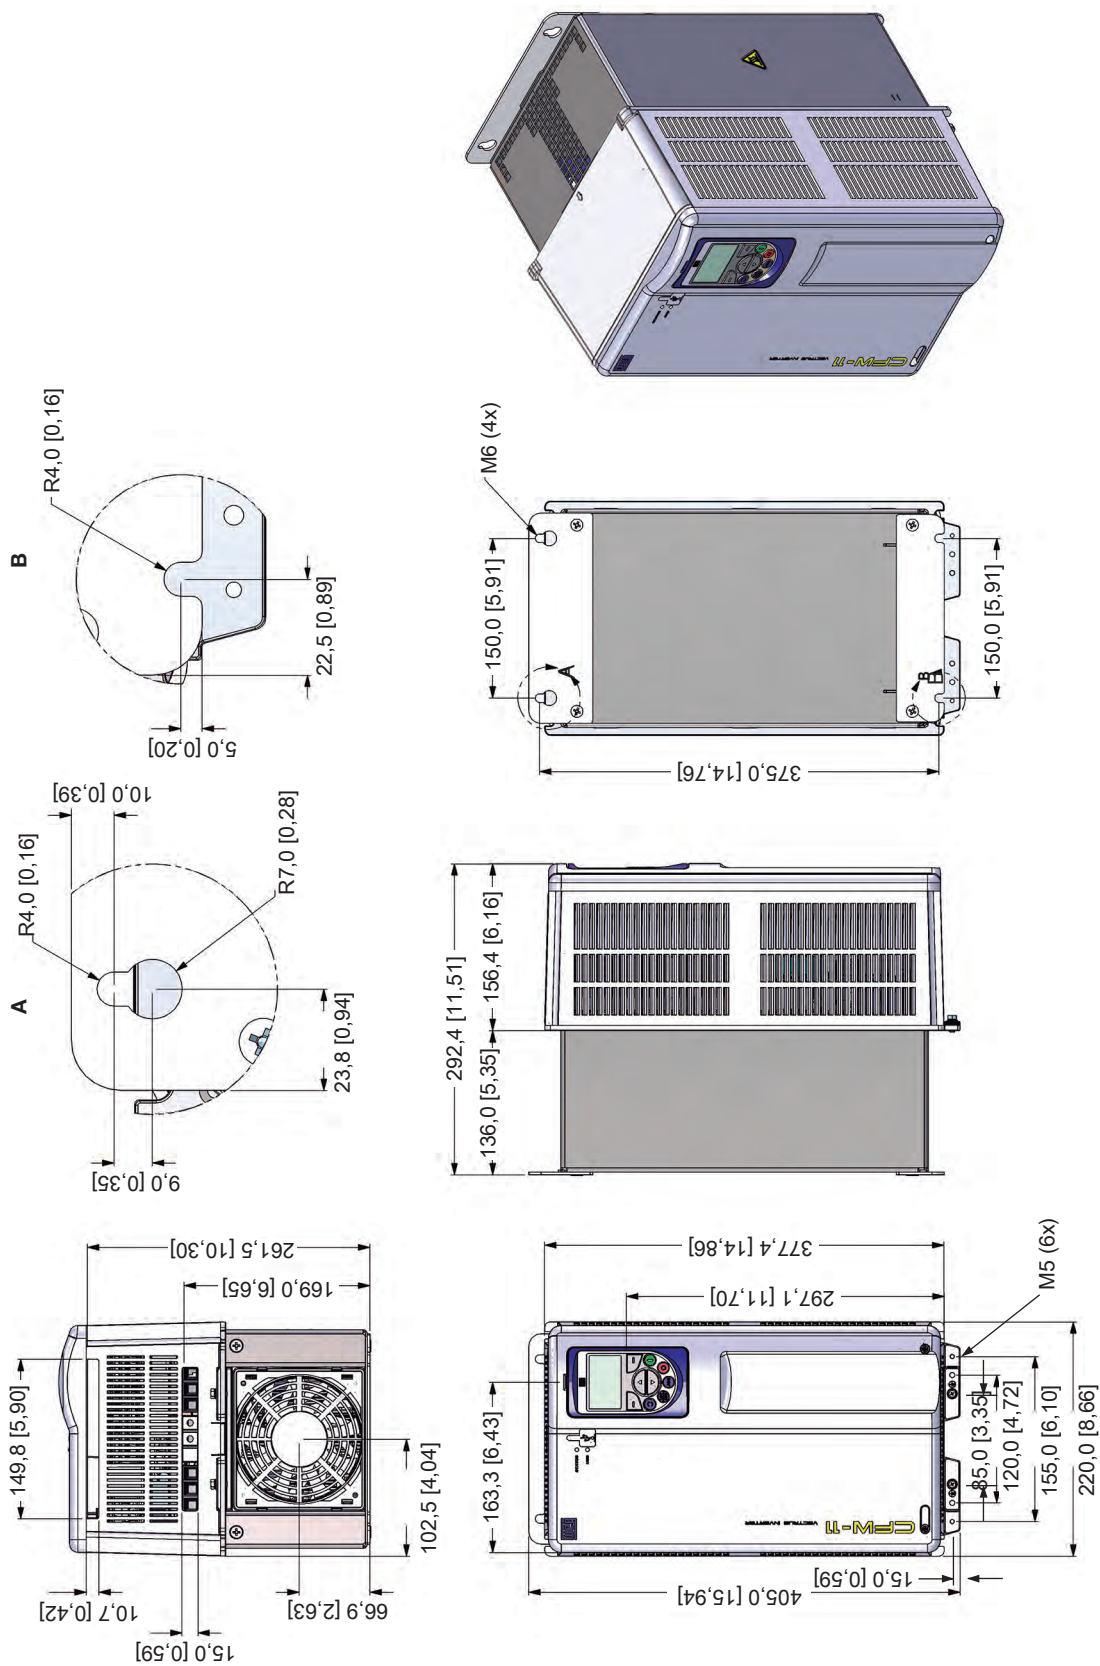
Габаритные размеры преобразователя, размер корпуса С, мм [дюйм.]
